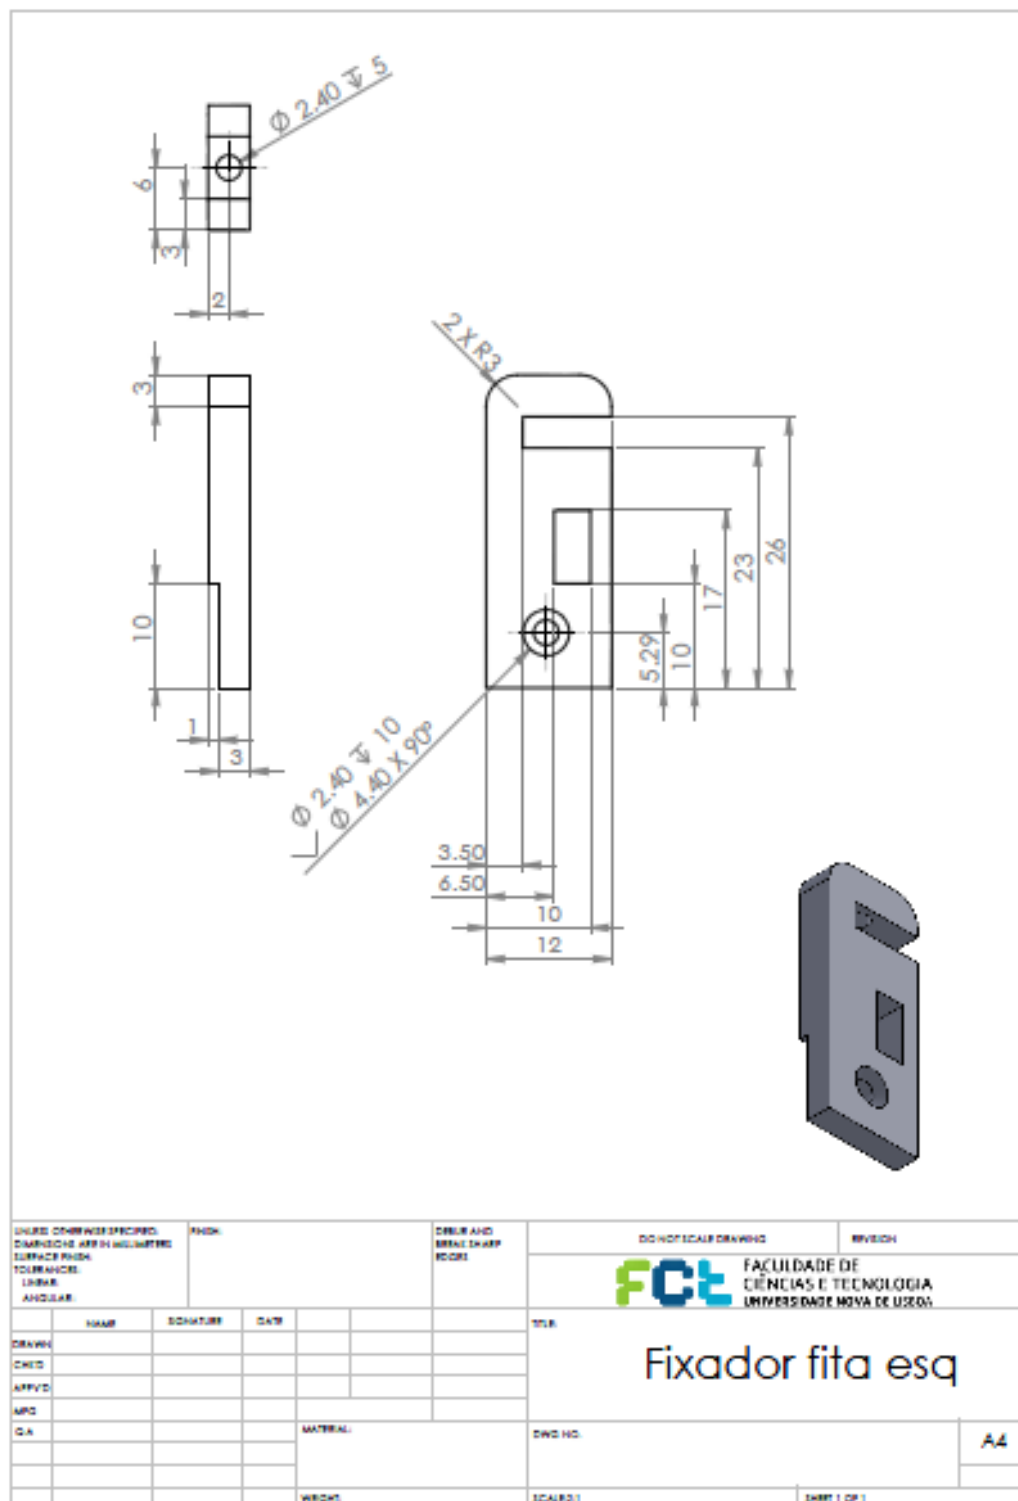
Desenho técnico do fixador da fita (esquerdo).
